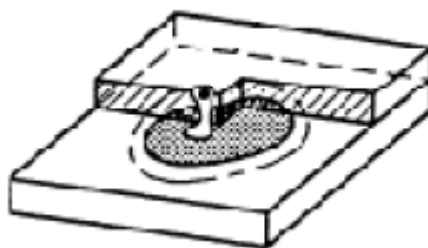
Ponto de soldadura com material fundido
